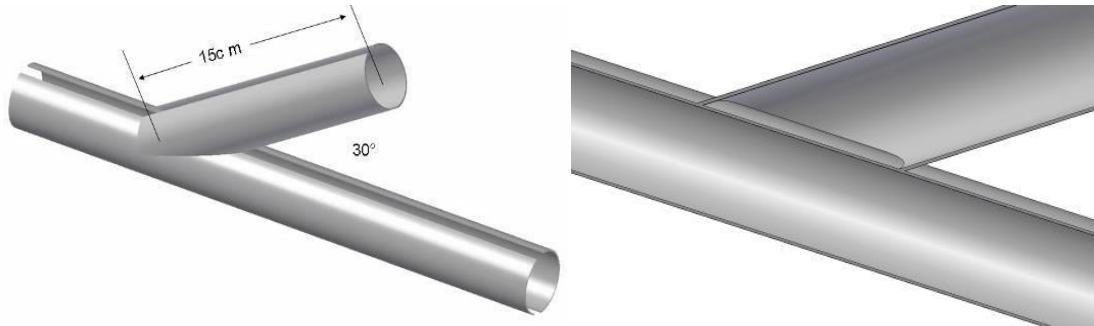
Ejemplo de prueba de inspección destructiva [8]
